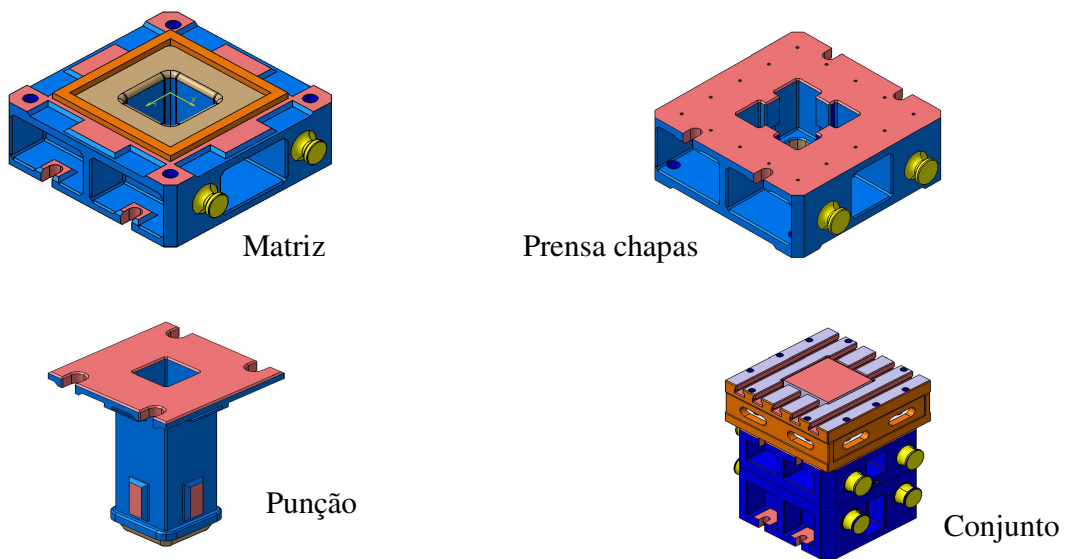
Desenho dos componentes da ferramenta 3D.
